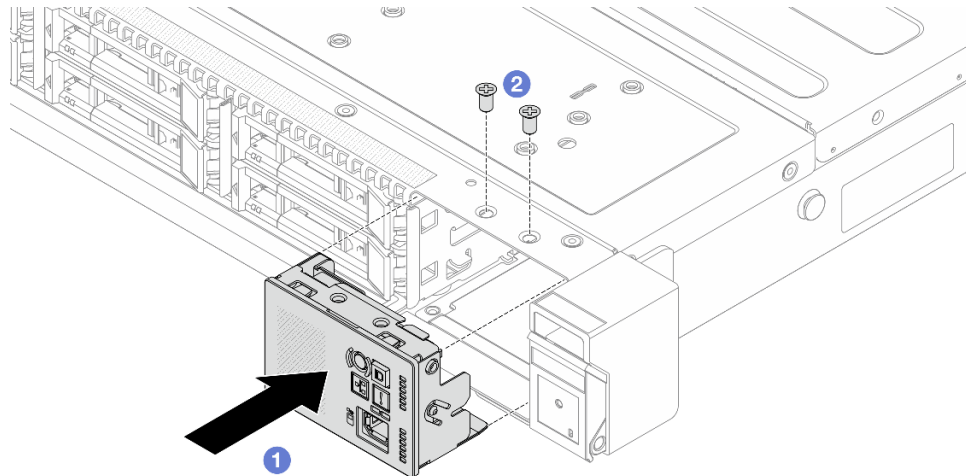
Instalación de un módulo de E/S frontal en el chasis de 2,5"
